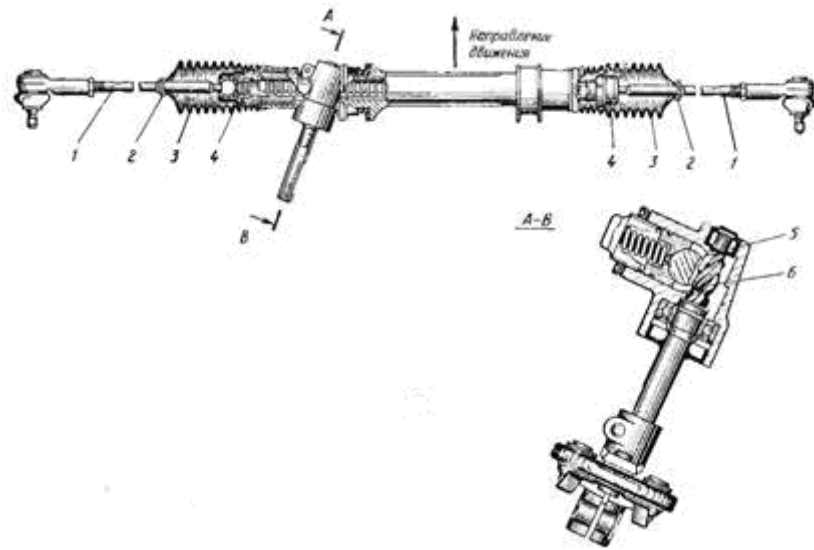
Боковое расположение шестерни при креплении боковых тяг к концам зубчатой рейки
